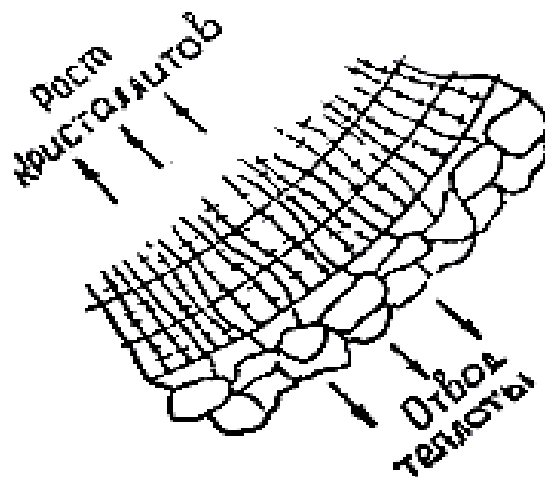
Схема кристаллизации сварного шва
